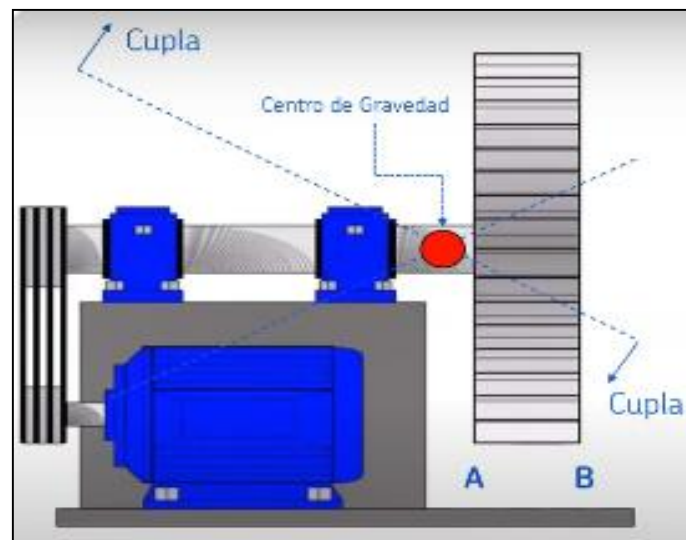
Rotor en voladizo desbalanceado (www.power-mi.com)
